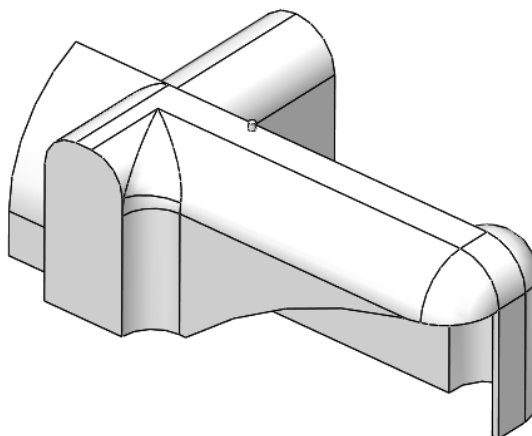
Общий вид корпусной детали со сложными криволинейными поверхностями
